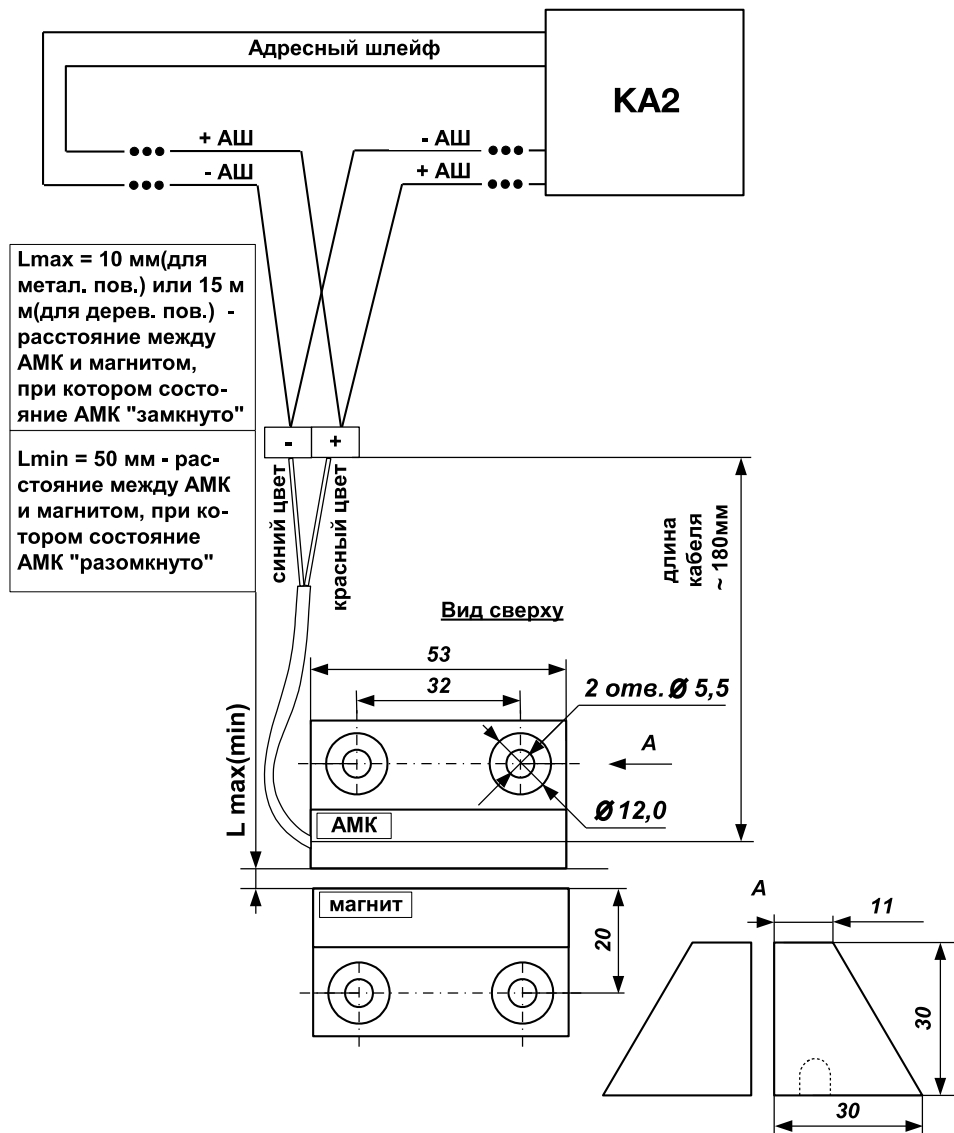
Конструкция, подключение, габаритные и присоединительные размеры
